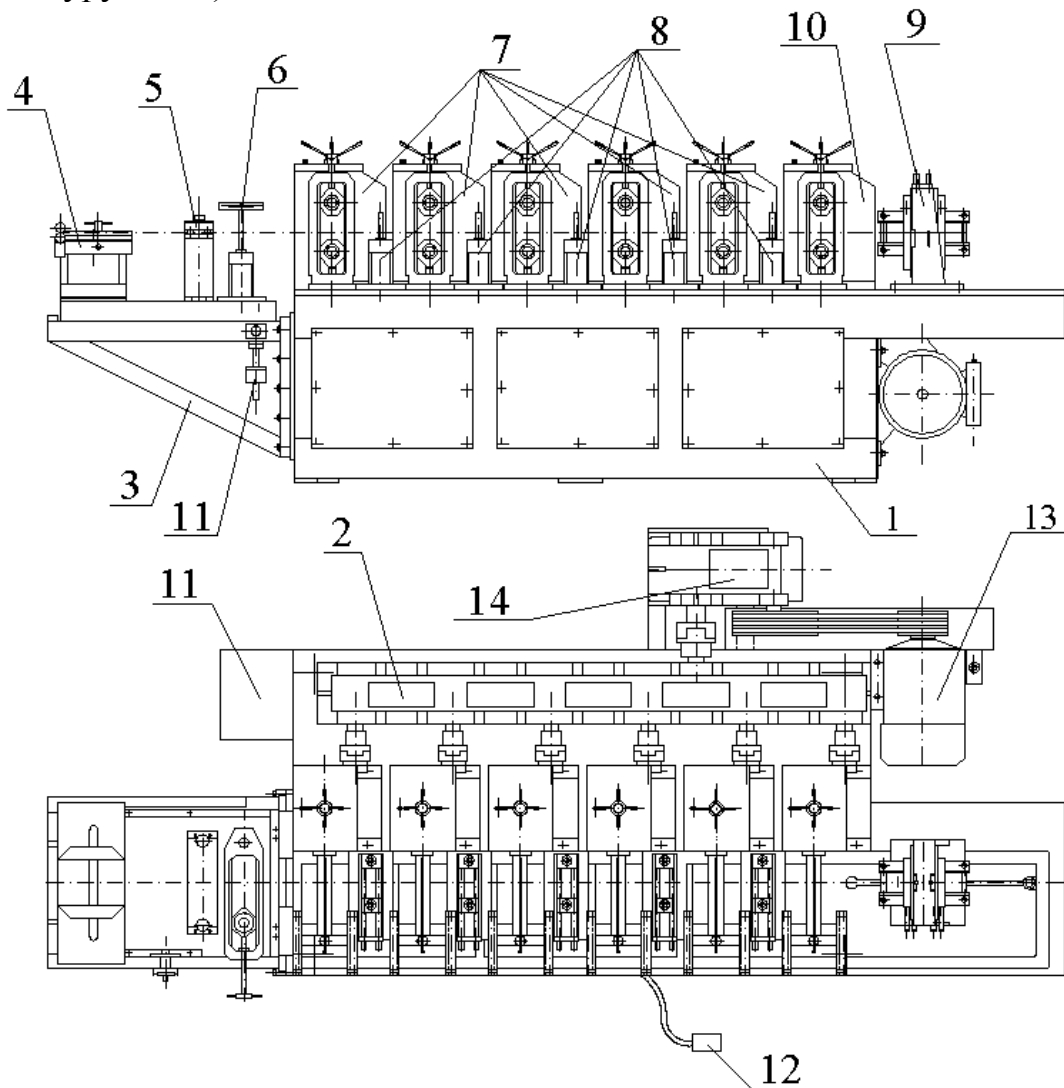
Схема гибочно-прокатного станка ГПС-350М6: 1 – станина; 2 – привод профилирующих клетей; 3 – рама; 4 – устройство направляющее; 5 – устройство для протирки и смазки ленты; 6 – клеть подготовительная; 7 – клеть предварительной формовки; 8 – межклетьевая проводка; 9 – устройство правильное; 10 – клеть окончательная формующая; 11 – привод клетки подготовительной; 12 – пульт управления; 13 – электродвигатель; 14 – редуктор.
